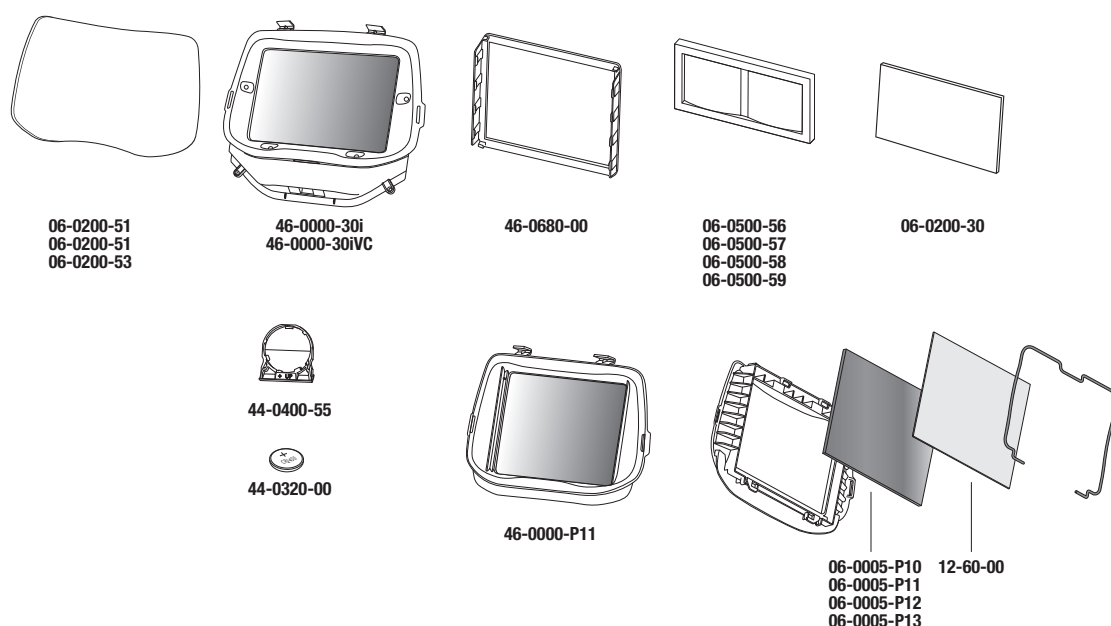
Pièces de rechange du filtre à lentille photosensible
